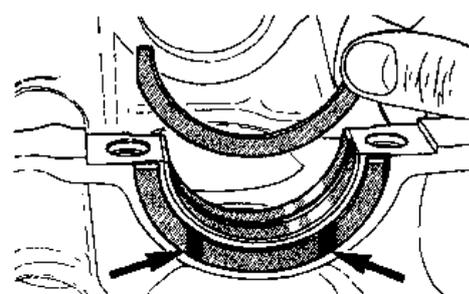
А.24. Положение упорных полуколец коленчатого вала
